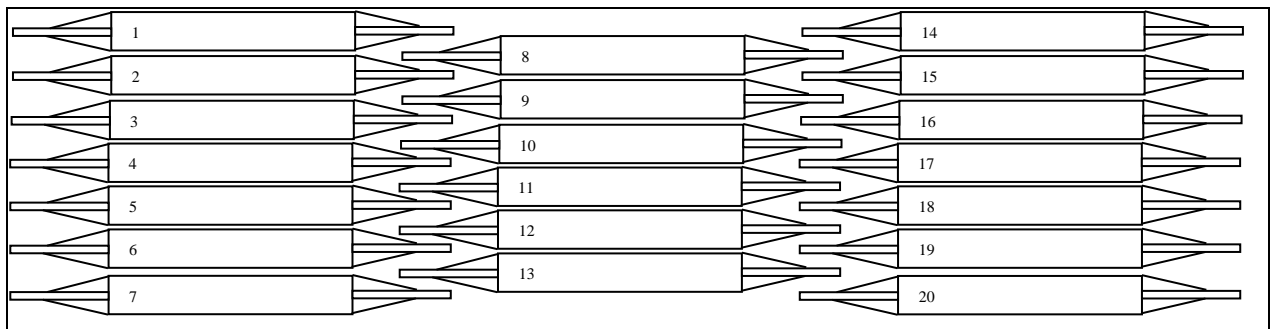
Схематичне розміщення заготовок полоза на сталюому листі
